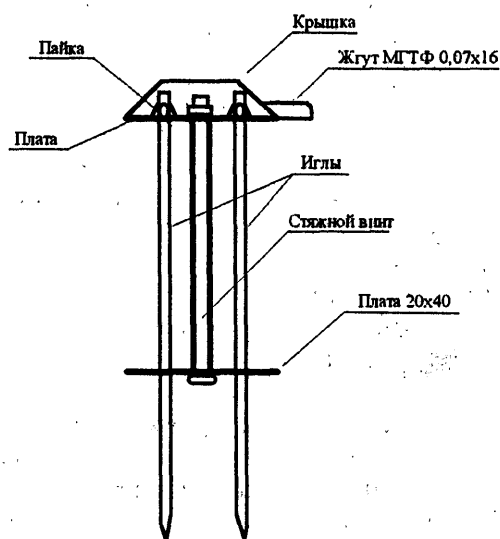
Конструкция щупа для прибора (М2:1)
